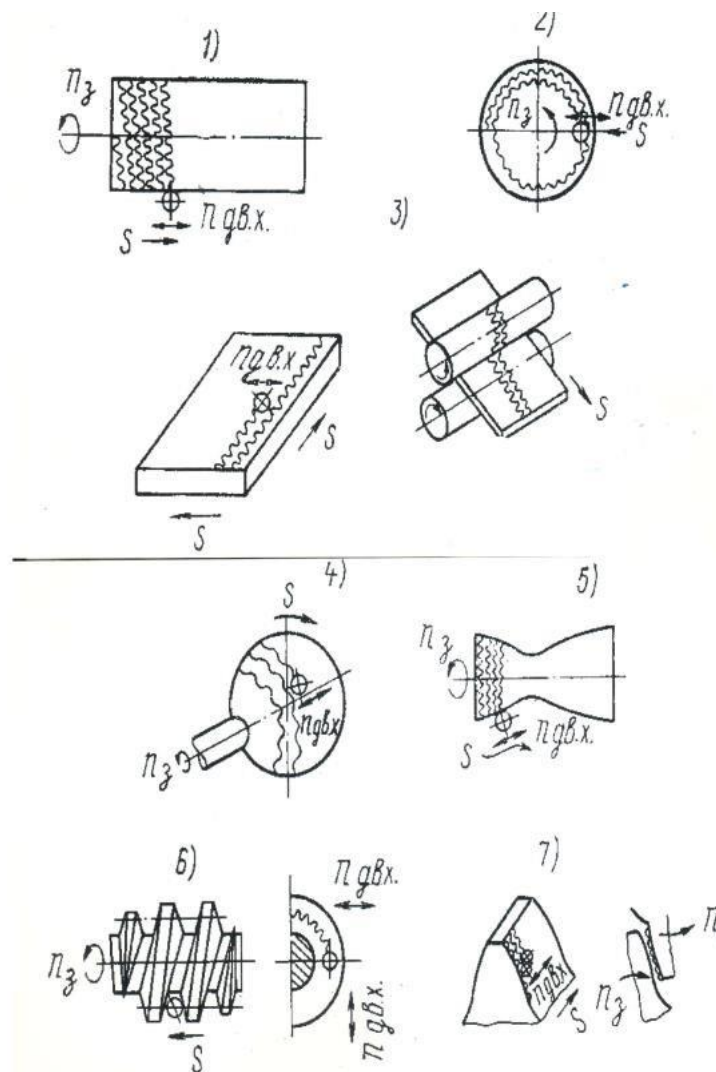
Схеми вібронакаткування поверхонь різної форми (1.-циліндрична, 2-торцева, 3-плоска, 4-сферична, 5- профільна, 6- гвинтова, 7-евольвентна).
